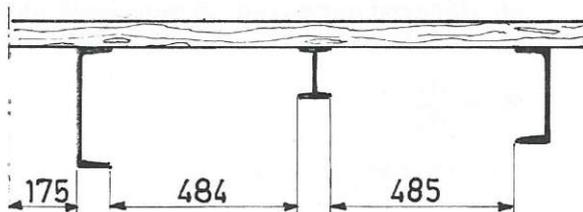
Longerons du wagon ORE avec planches en chêne de section 200 x 70 mm
